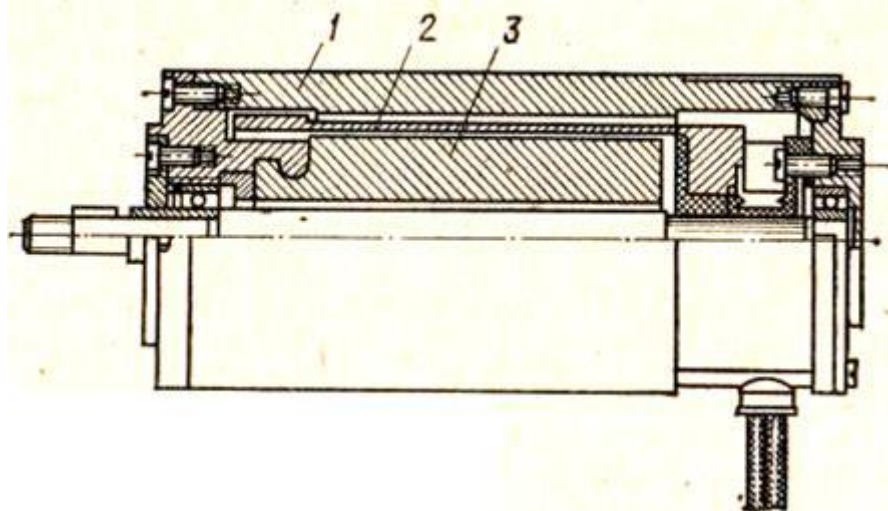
Исполнительный двигатель постоянного тока с полым якорем серии ДПР: 1- станина (внешний статор); 2- полый якорь; 3 – внутренний статор.
